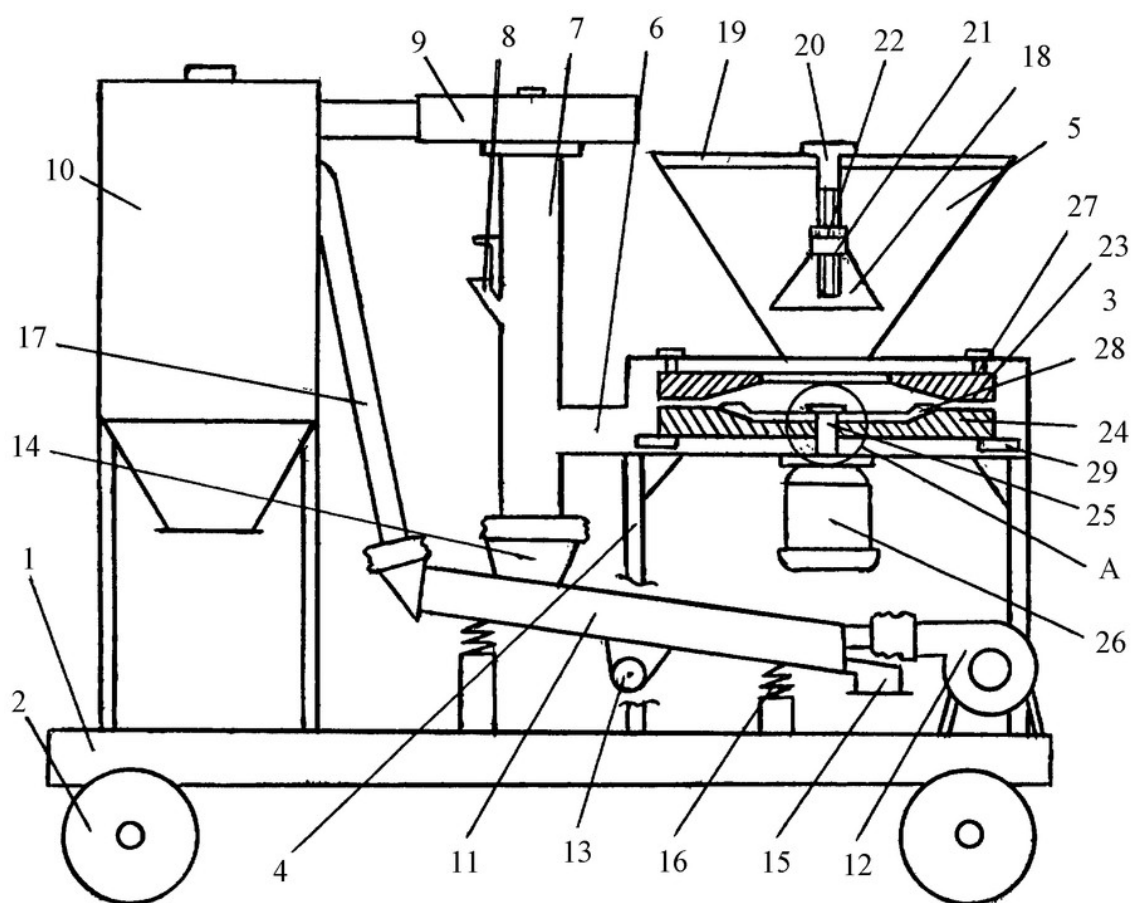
Шелушильная установка BUHLER-MIAG.
